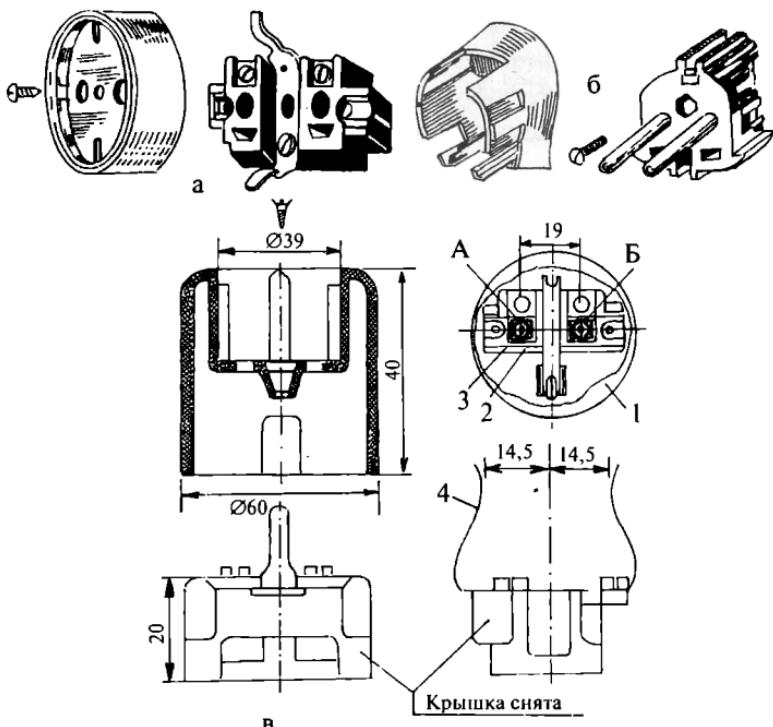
Двухполюсный соединитель с боковыми заземляющими контактами на 10–16 А, 250 В для открытой установки: а — розетки; б — вилки; в — розетка в разрезе: 1 — крышка; 2 — основание; 3 — гнездо; 4 — заземляющие контакты («усы»)
